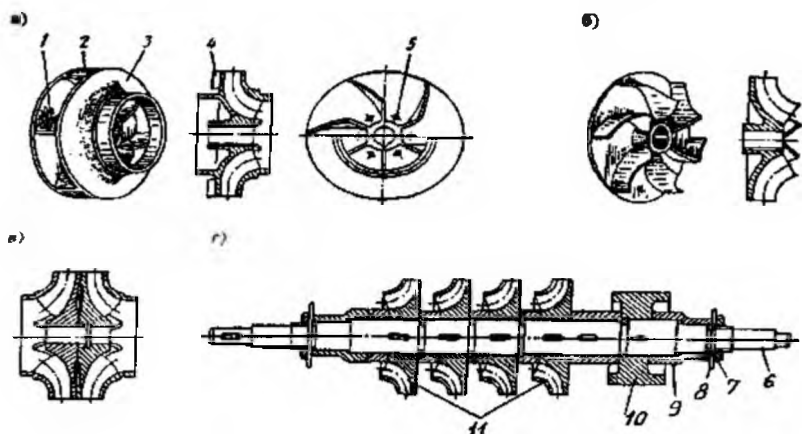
Рабочее колесо и ротор центробежного насоса:
